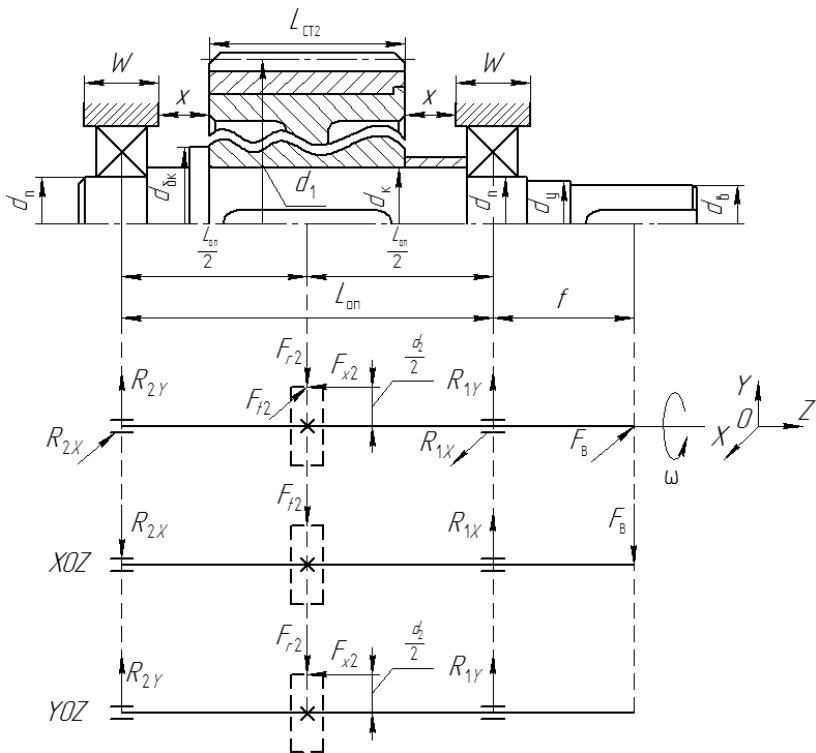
Схема нагружения тихоходного вала червячного одноступенчатого редуктора
